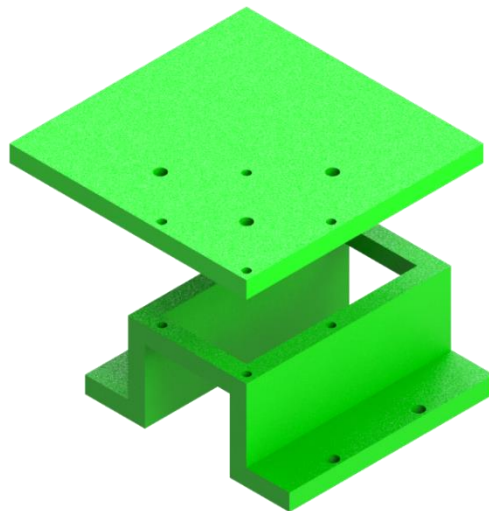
Diseño de soporte para acoplamiento explosionado destacando puntos de fijación
